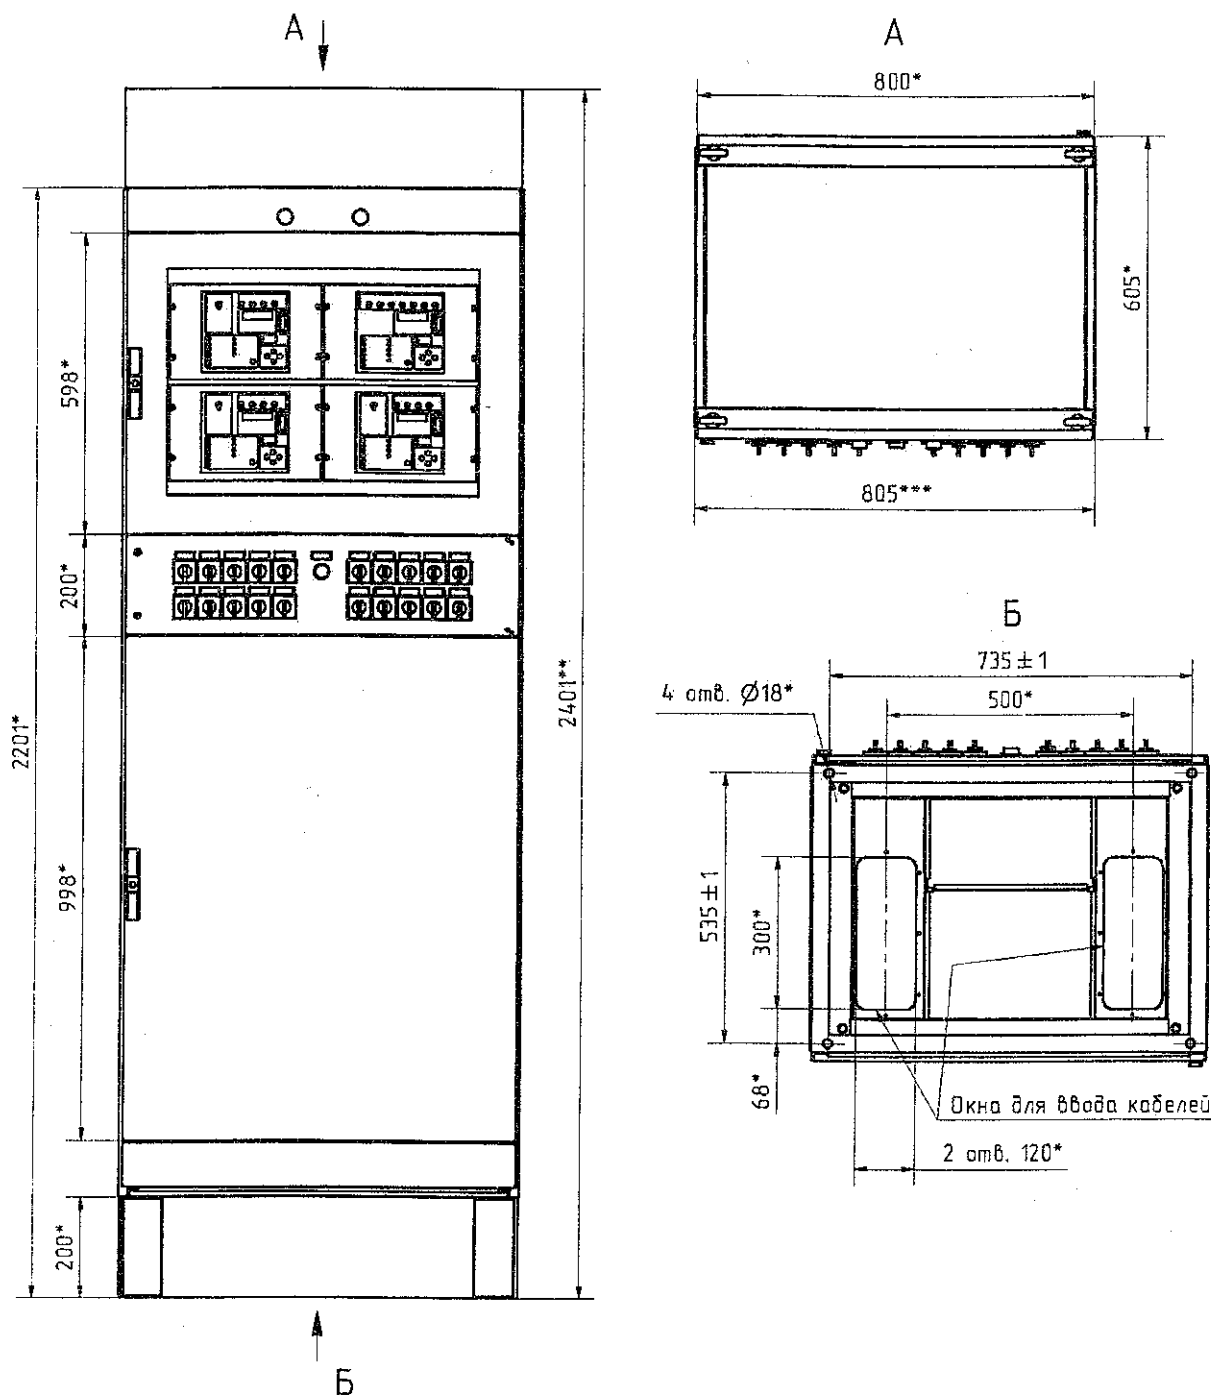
Габаритный чертеж шкафа серии ШЭРА (с боковыми панелями)
